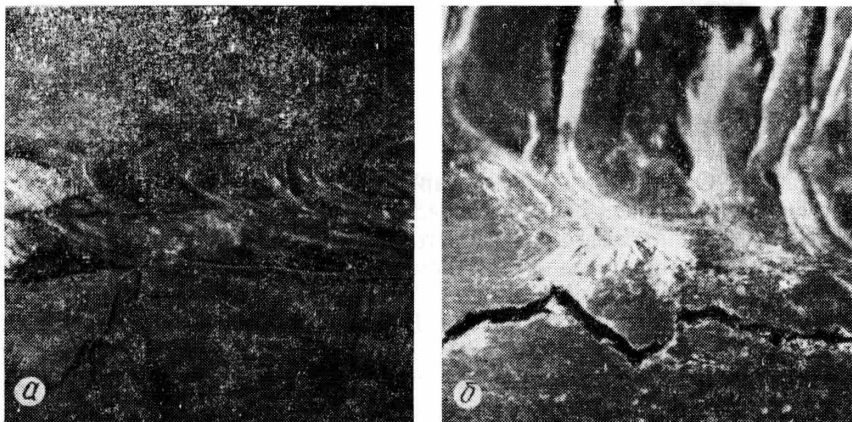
Коррозионные трещины в сварных соединениях стали Ст. 3:
